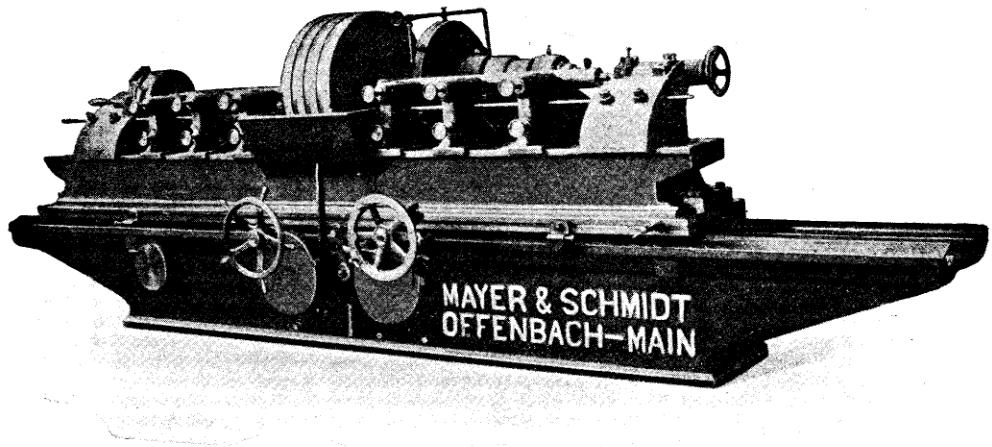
Machine automatique à rectifier les tiges de pistons ou de tiroirs.
